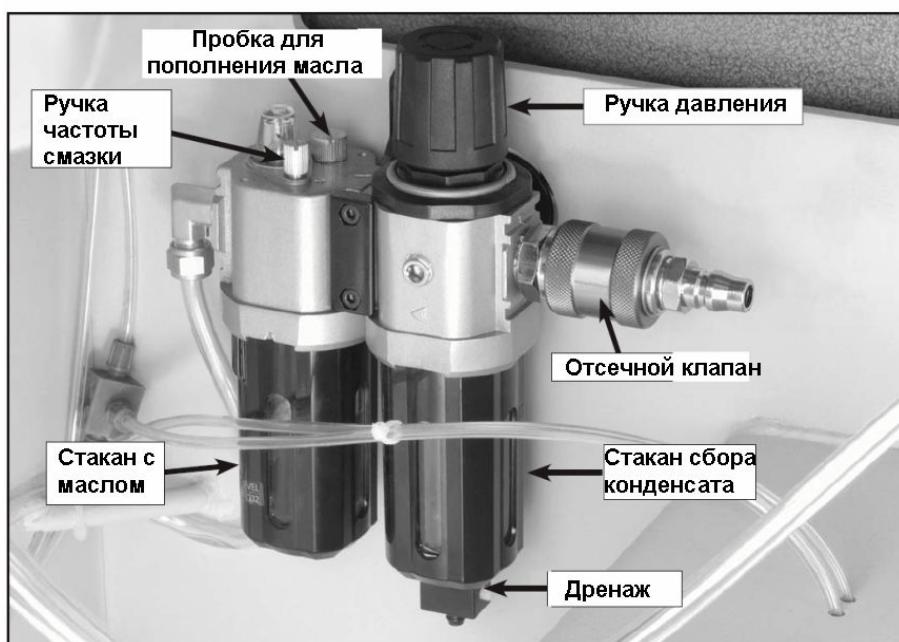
Группа "фильтр-редуктор-лубрикатор" пневматической системы станка.
